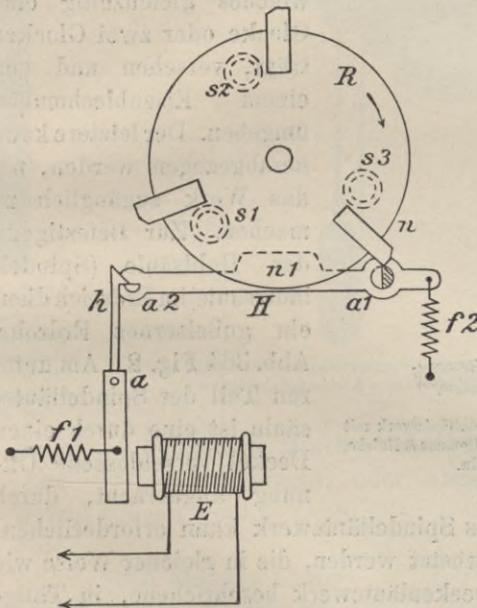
Elektrische Auslösung des Spindel- oder Einradläutewerks von Siemens & Halske, Berlin.
